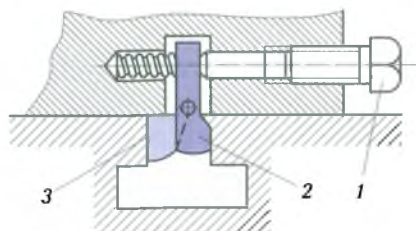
Схема использования шпонки и прижимного механизма для повышения точности установки приспособления:
